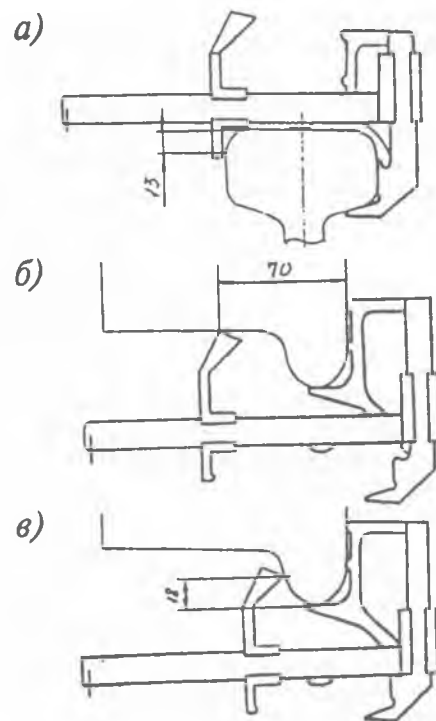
Положение скобы СК-6 при измерении: а — бокового и вертикального износа головки рельса; б — проката бандажа (обода) колеса; в — износа гребня колеса
